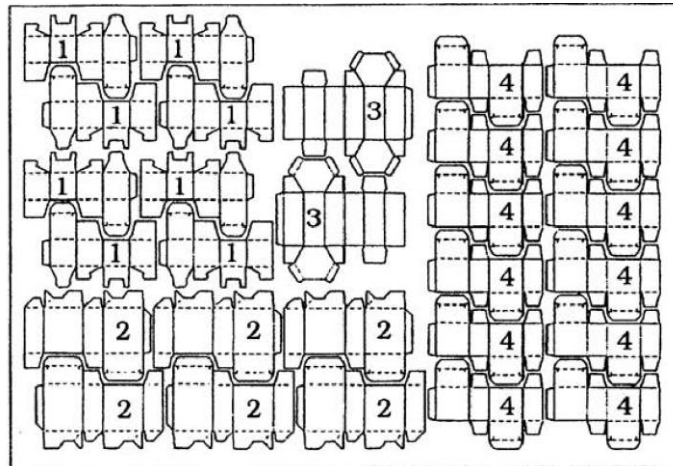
Позиціонування розгортки кількох коробок на форматі заготовки з картону
